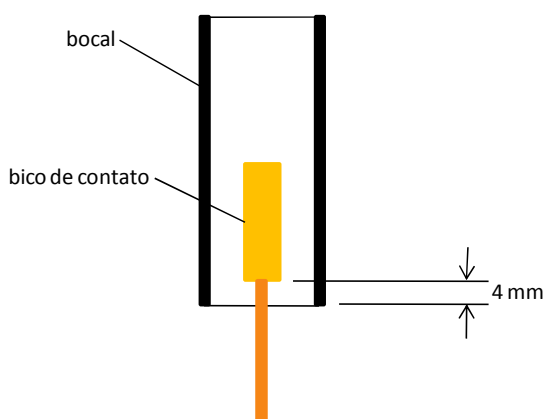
Posicionamento do bico de contato em relação ao bocal da tocha utilizado nas soldagens no modo goticular
